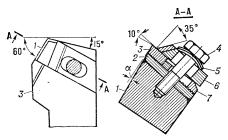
Резец конструкции ЦНИИТМаш с механическим закреплением пластинки: 1 — державка; 2 — подкладка; 3 — пластина; 4 — болт; 5 — шайба; 6 — прижим; 7 — передвижной упор.
